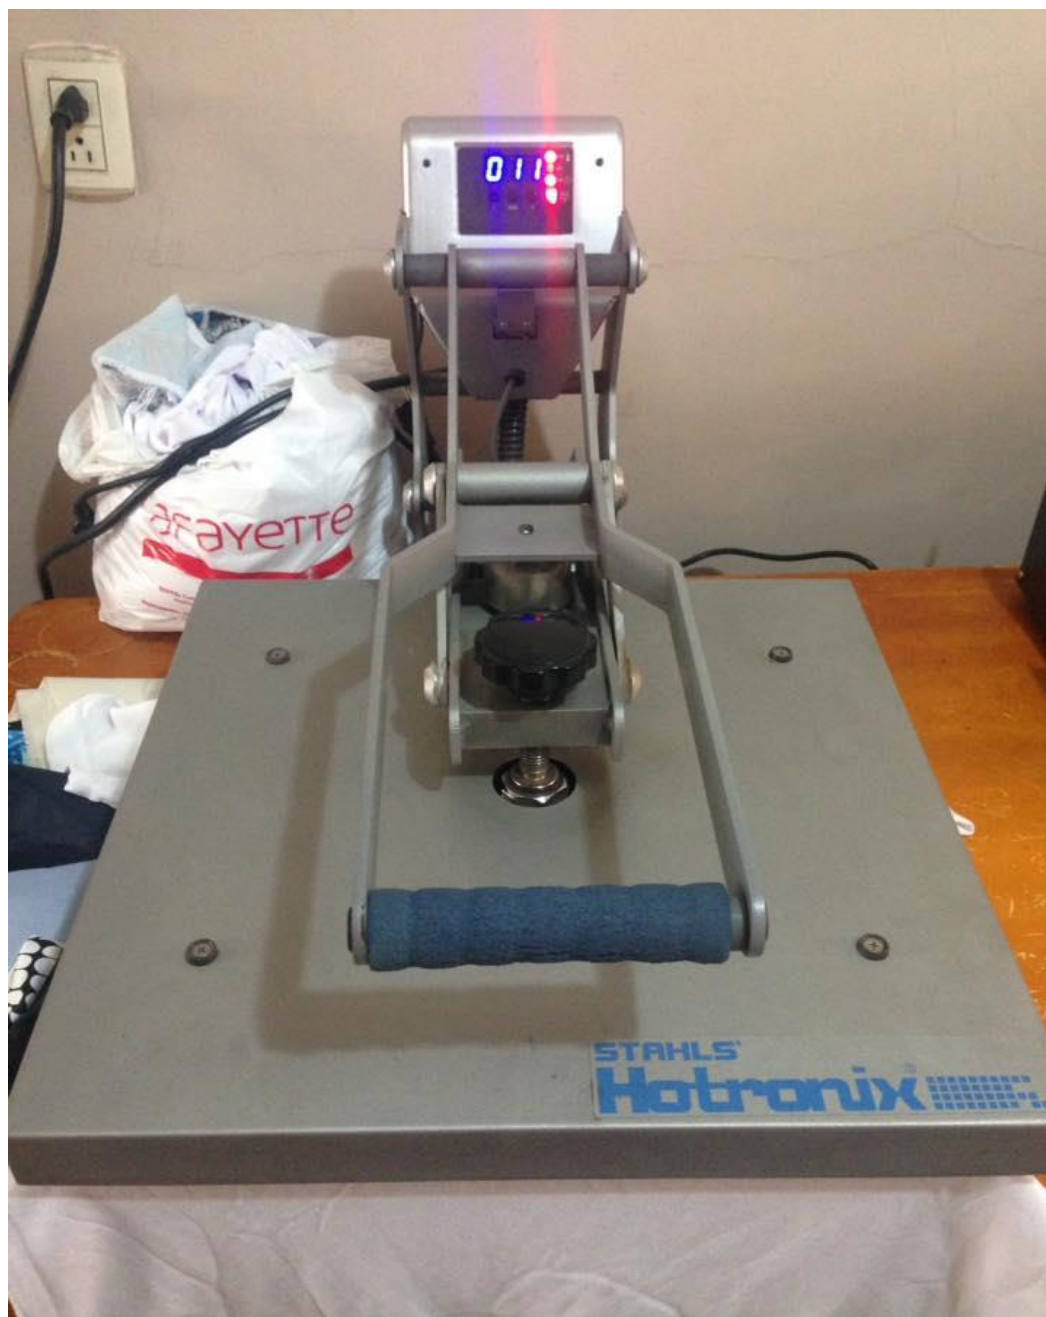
Bajar la plancha con cuidado por 12 segundos y luego levantarla.
